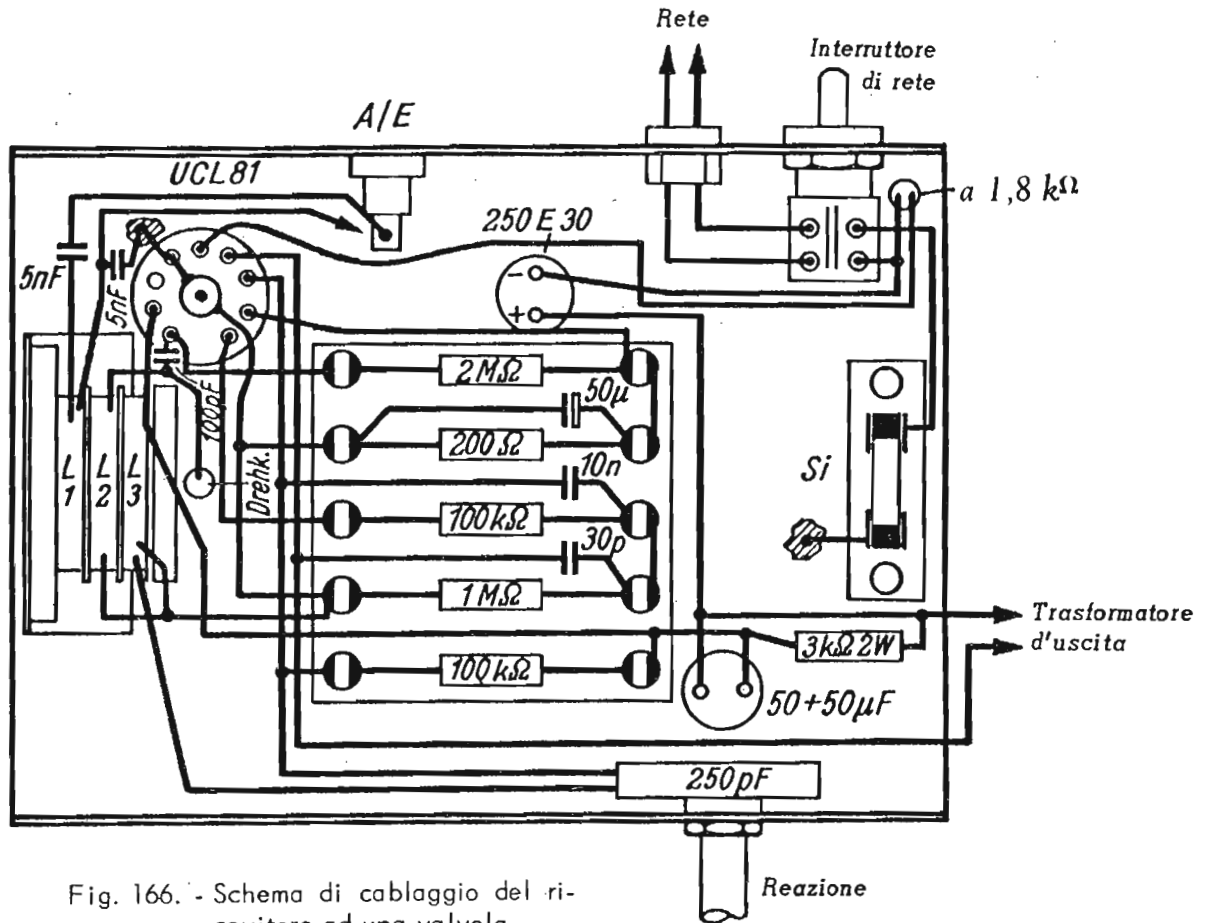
Schema di cablaggio del ricevitore ad una valvola.
